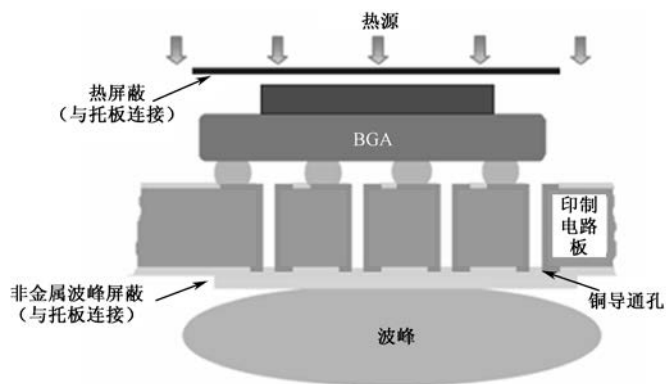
在波峰焊接过程中，防止 PCB 顶部 BGA 焊点再流的方法
